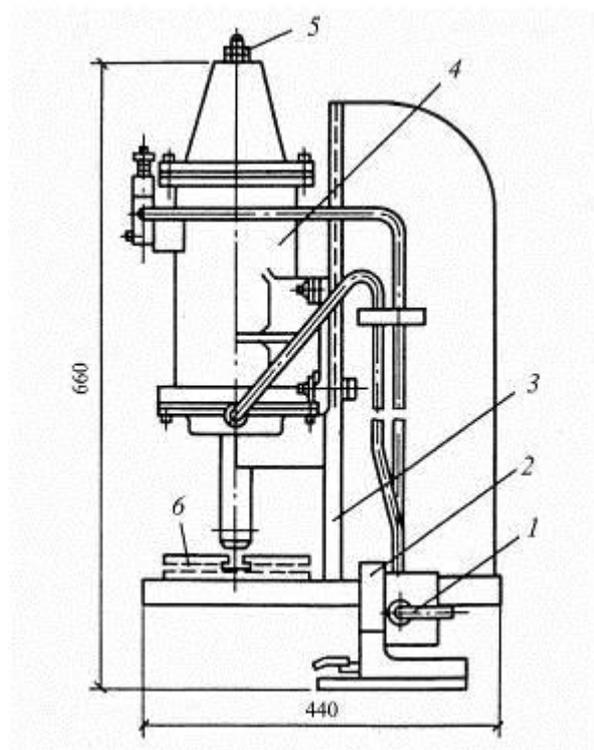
Пресс пневматический: 1 — распределительный кран; 2 — станина; 3 — направляющие; 4 — пневмоцилиндр; 5 — регулировочные гайки; 6 — стол
